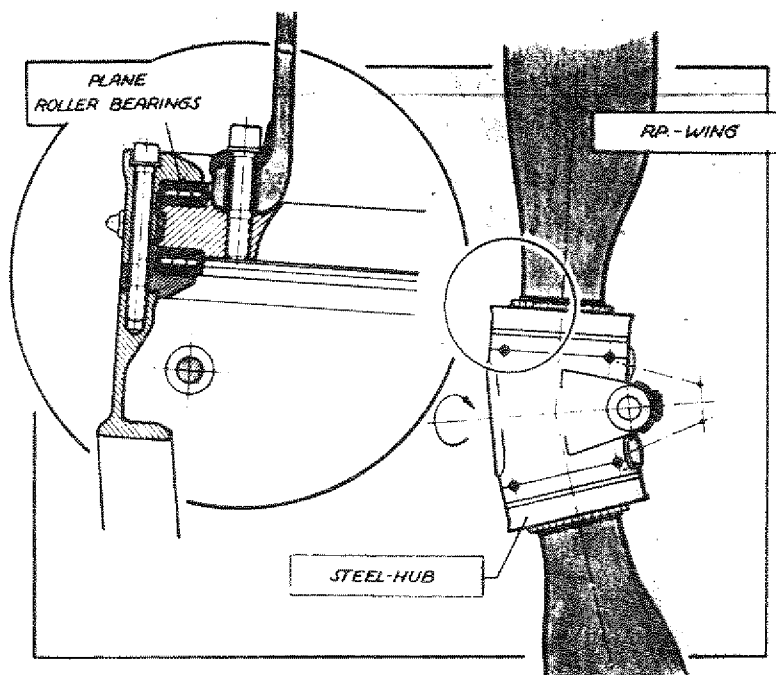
W 34/100 Lagerzeichnung (Flügelverstellung)
